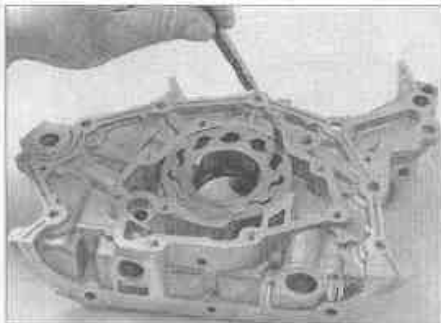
,а. Щупом измерьте зазор между приводным ротором и корпусом
